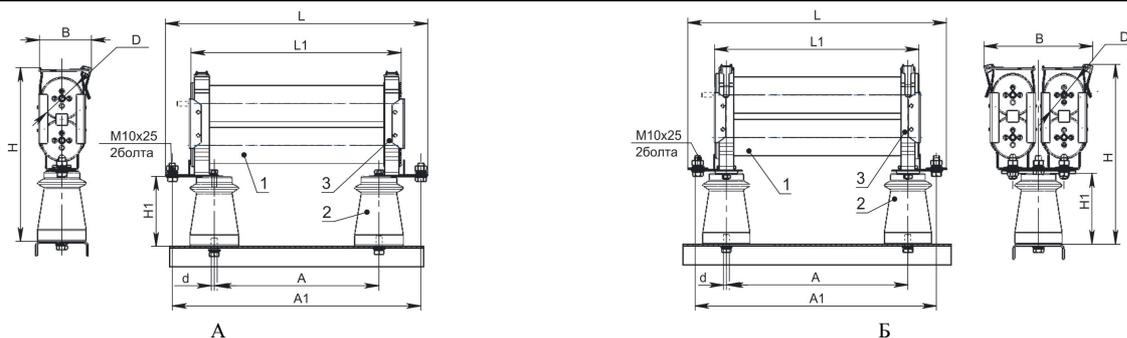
Габаритные и установочные размеры предохранителей ПКТ-103, ПКТ-104.
